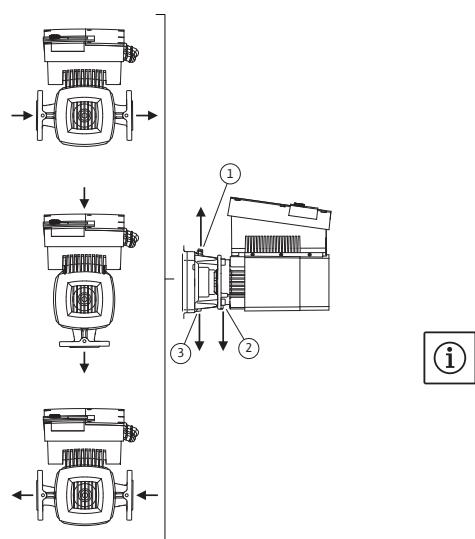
Godkjente monteringsstillinger med horisontal motoraksel
